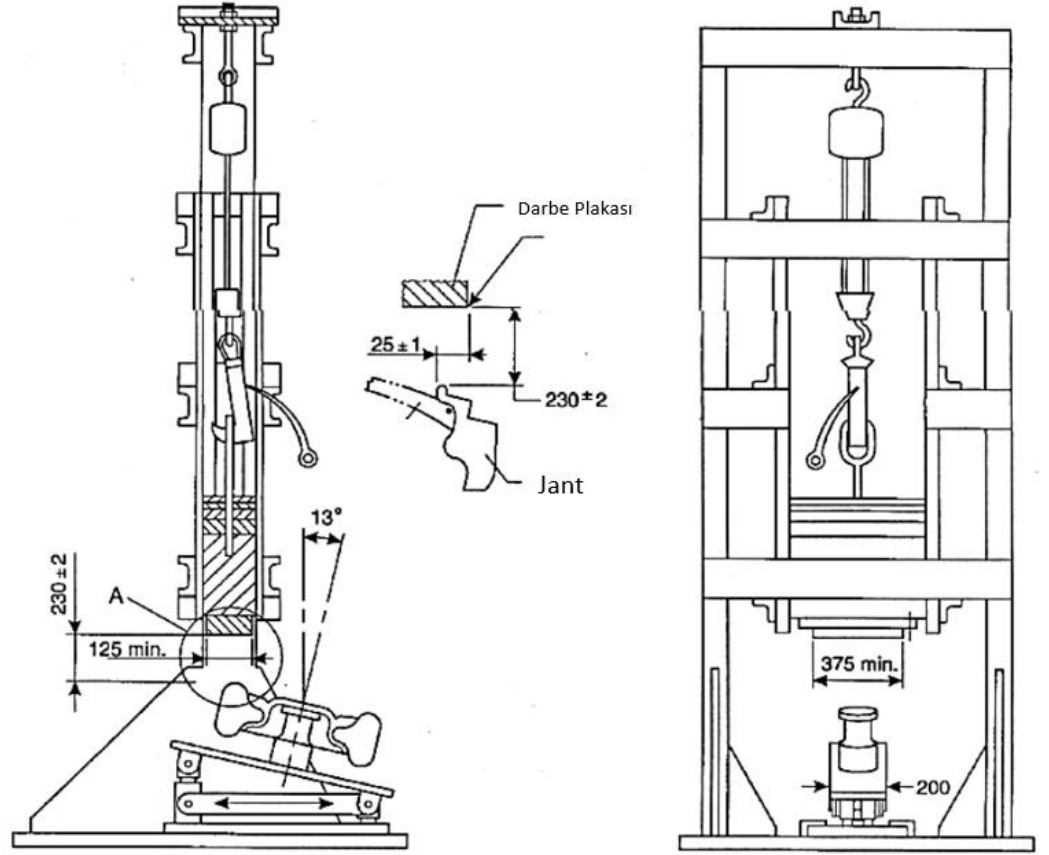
Darbe testine ilişkin jant montaj bölgesi şeması
